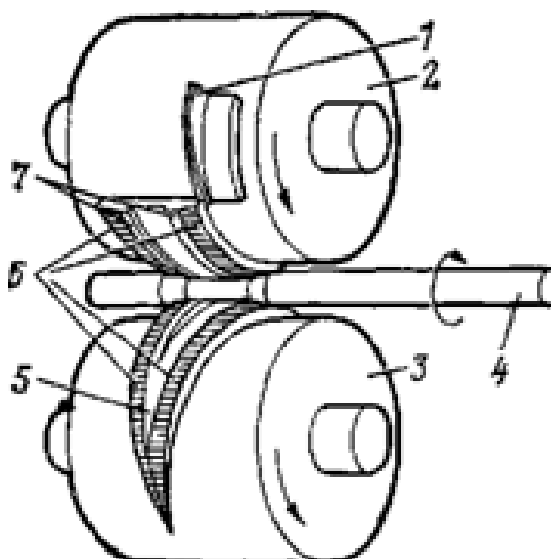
Схема поперечно-клинової прокатки; 1 - початок струмка лівого валка; 2 - лівий валок; 3 - правий валок; 4 - заготовка; 5 -початок струмка правого валка; 6 - струмки; 7 - реборди
